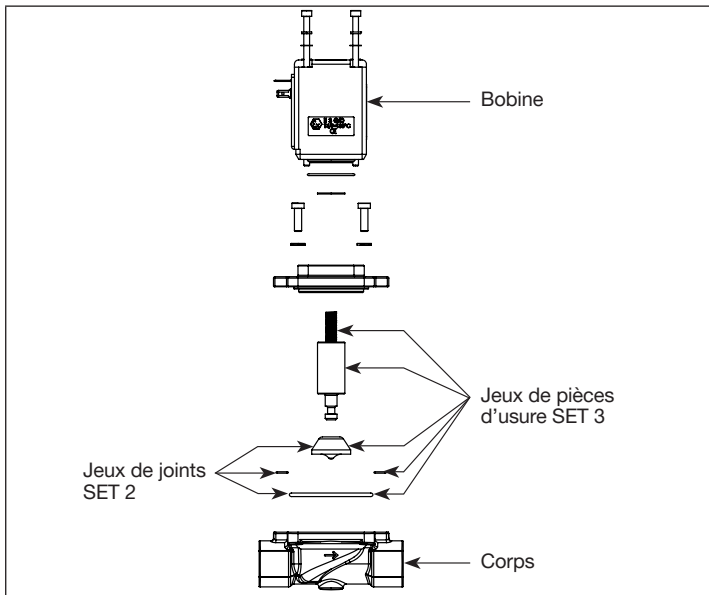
Aperçut jeux de pièces de rechange Type 0283
